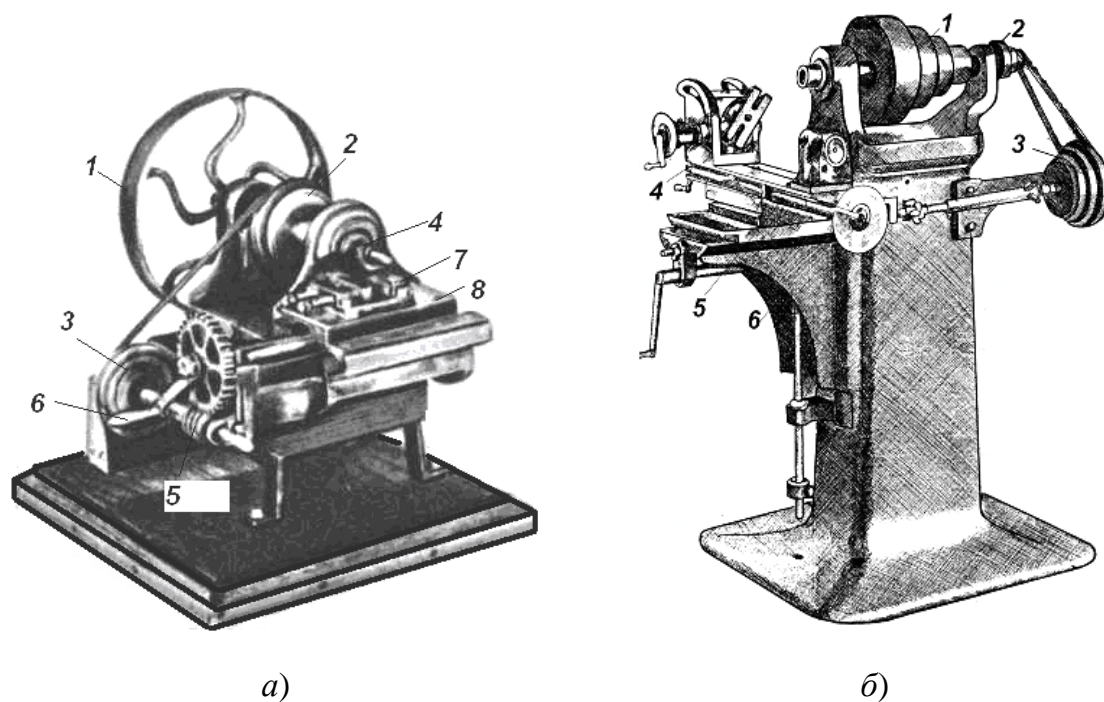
Горизонтально-фрезерные станки Э. Уитни
